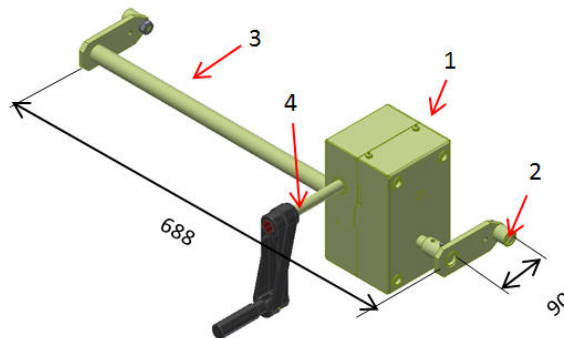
Схема узла блокировки и редукции ВЭ К-37.
